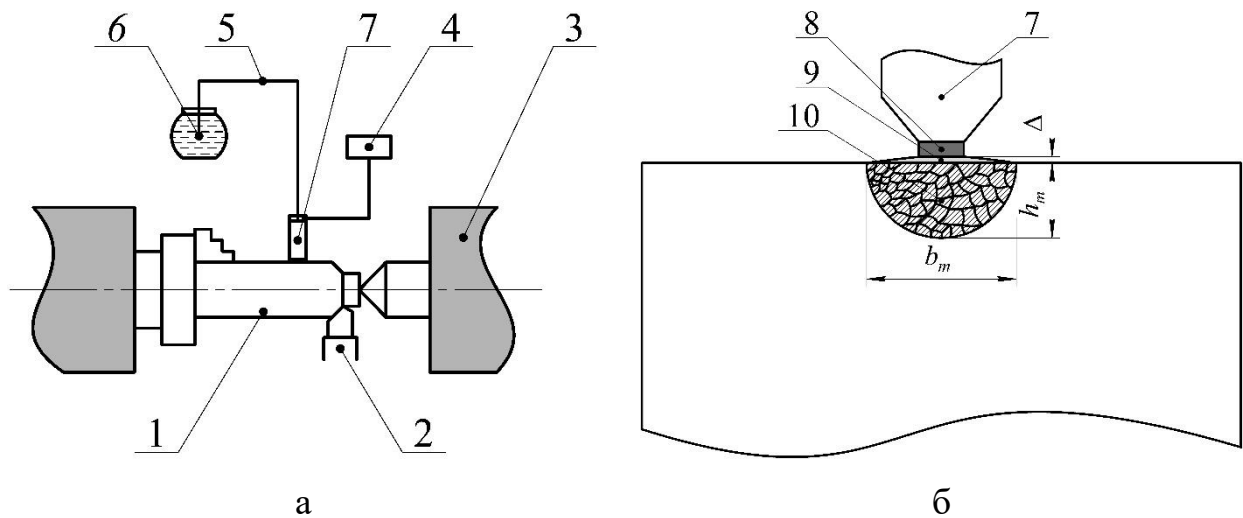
Схема технологической установки с устройством подачи жидкого азота (составлено автором), где: а) 1 – заготовка; 2 – режущий инструмент; 3 – станок; 4 – баллон с сжатым воздухом; 5 – переливное устройство; 6 – сосуд Дьюара; б) 7 – устройство подачи жидкого азота; 8 – контактный элемент; 9 – жидкий азот; 10 – метастабильная структура
